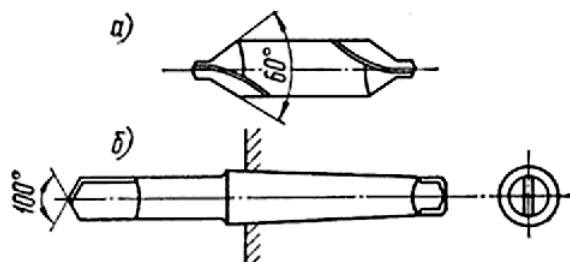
Типы центровочных сверл для зацентровки отверстий:
